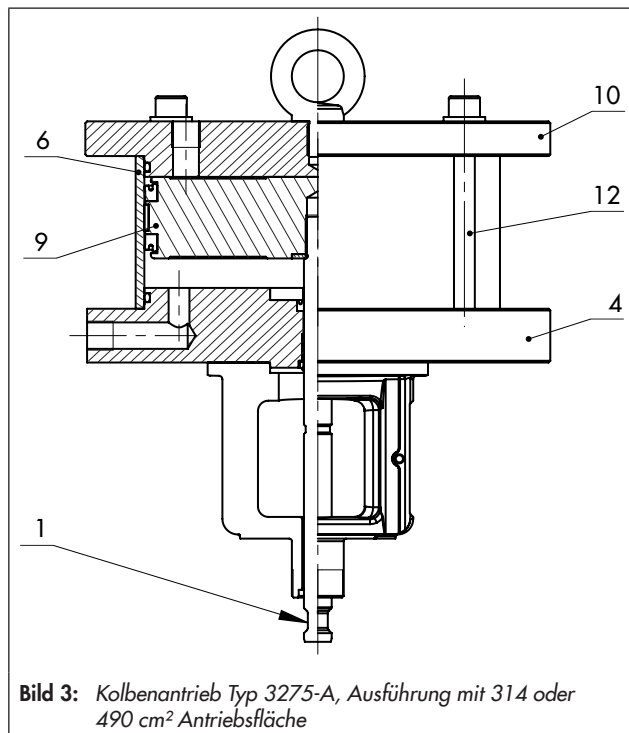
Kolbenantrieb Typ 3275-A, Ausführung mit 314 oder 490 cm² Antriebsfläche
